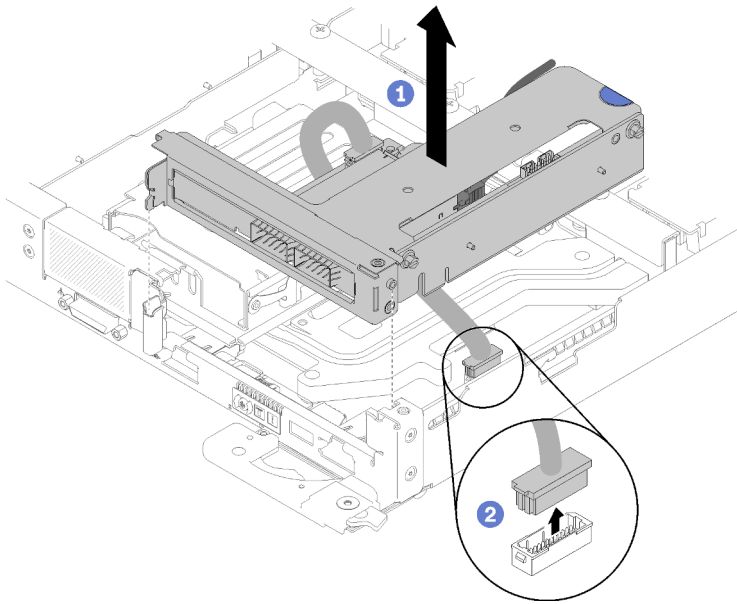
Retrait de l'assemblage de boîtier de connecteur de bus PCIe
